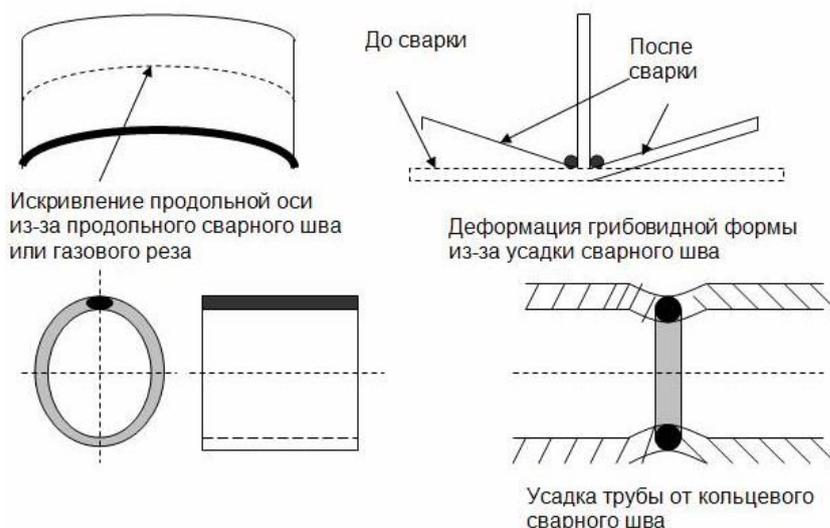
Примеры деформаций при сварке и резке
